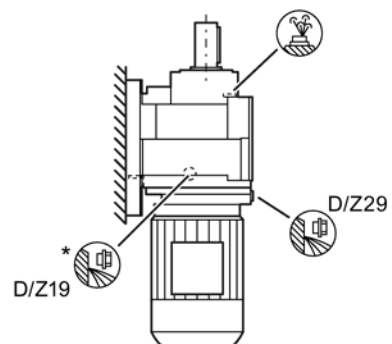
Монтажные положения для цилиндрического редуктора EF/EZ в исполнении с фланцем, типоразмы 39 - 149
